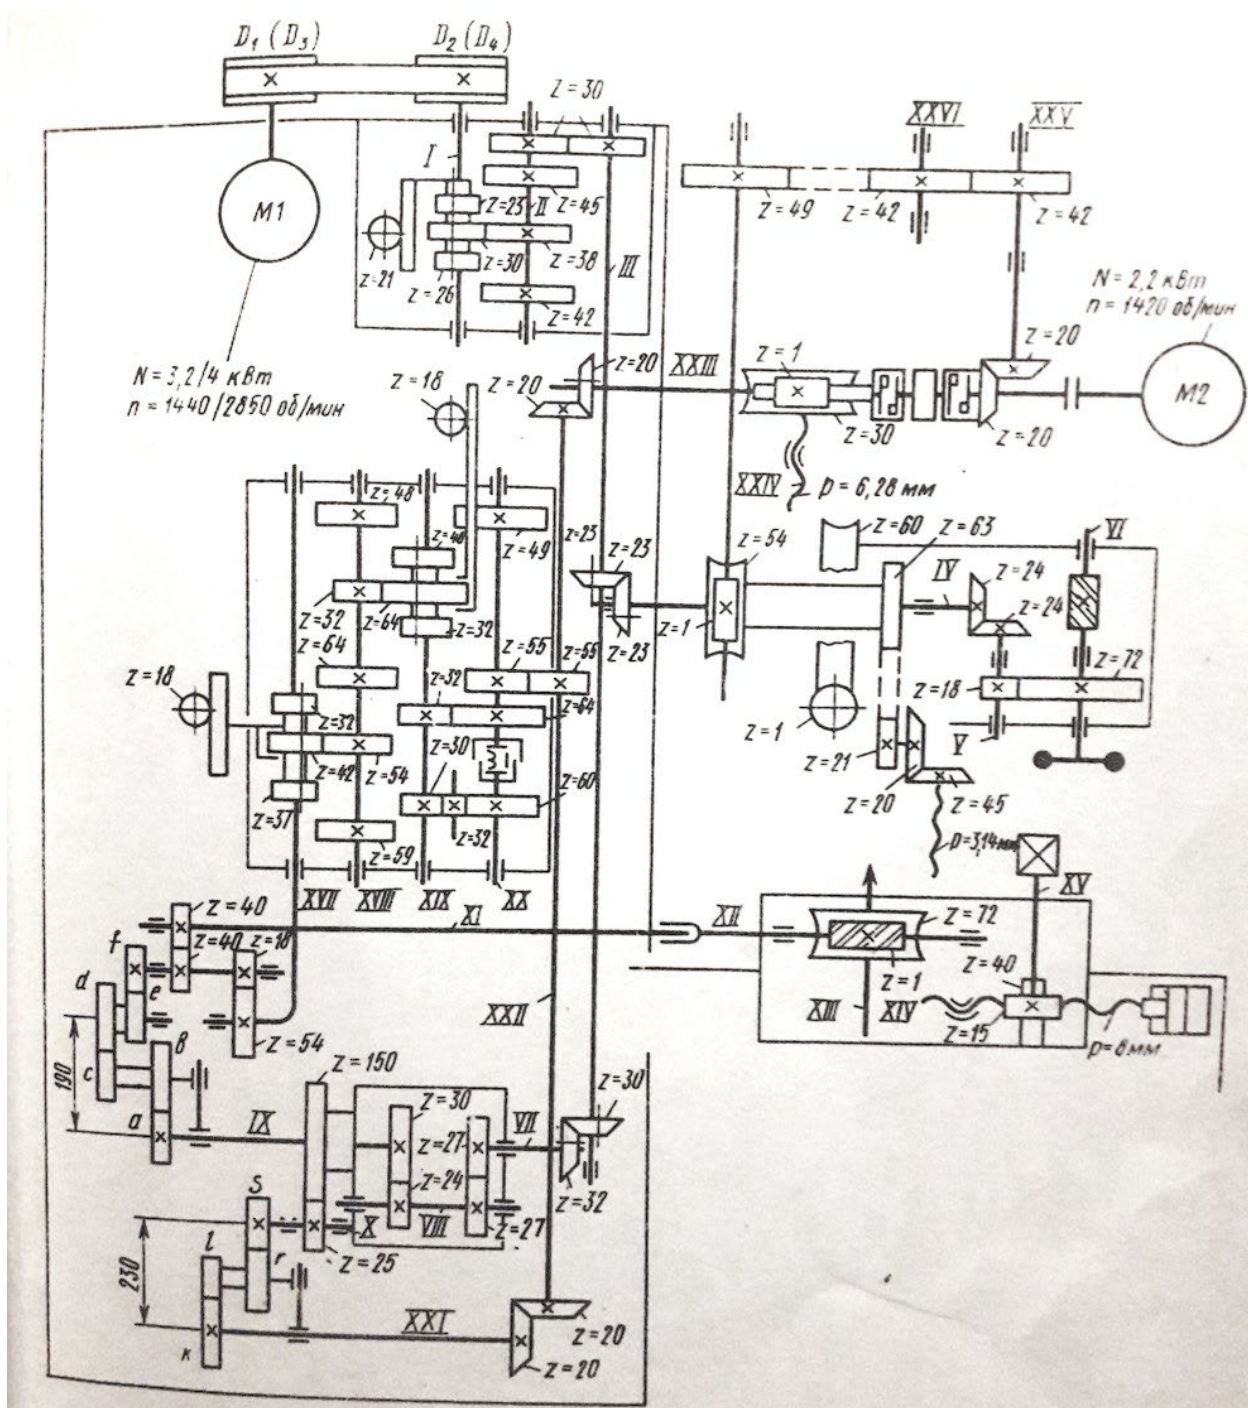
Кинематическая схема зубофрезерного станка модели 53А30
